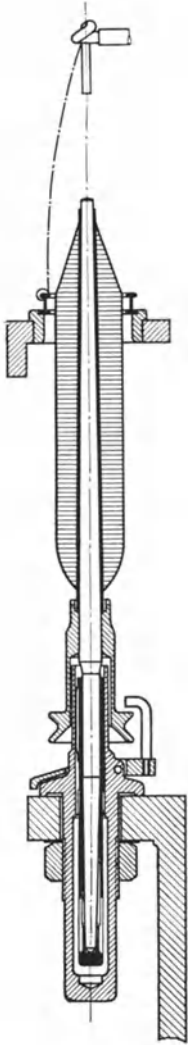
Flexible Spindel mit Gleitlager für Pincops (Deutsche Spinnereimaschinenbau A.-G., Ingolstadt).
